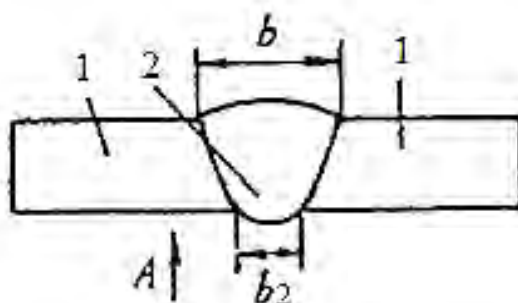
Вид спереди контрольного образца [44]: 1 – свариваемые пластины; 2 – сварной шов
